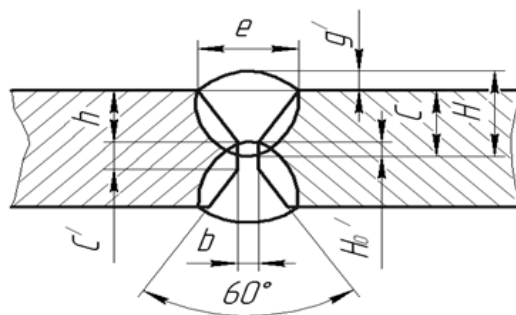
Конструктивні елементи підготовлених кромки зварних деталей (тип з'єднання – С21)
